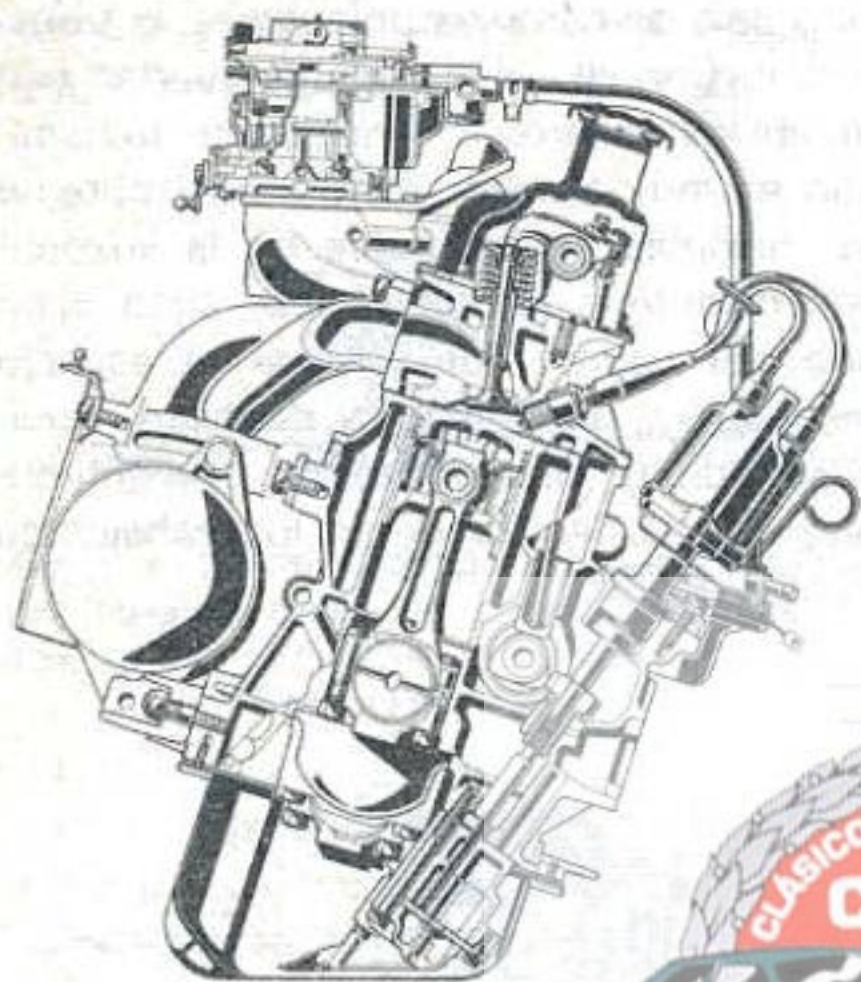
Corte transversal del motor que desarrolla 67 CV (DIN).
